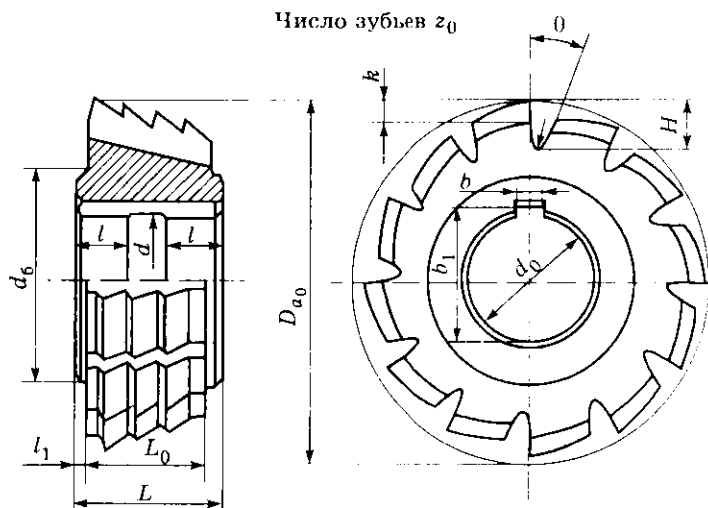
Конструктивные элементы фрезы для нарезания храповых колес
